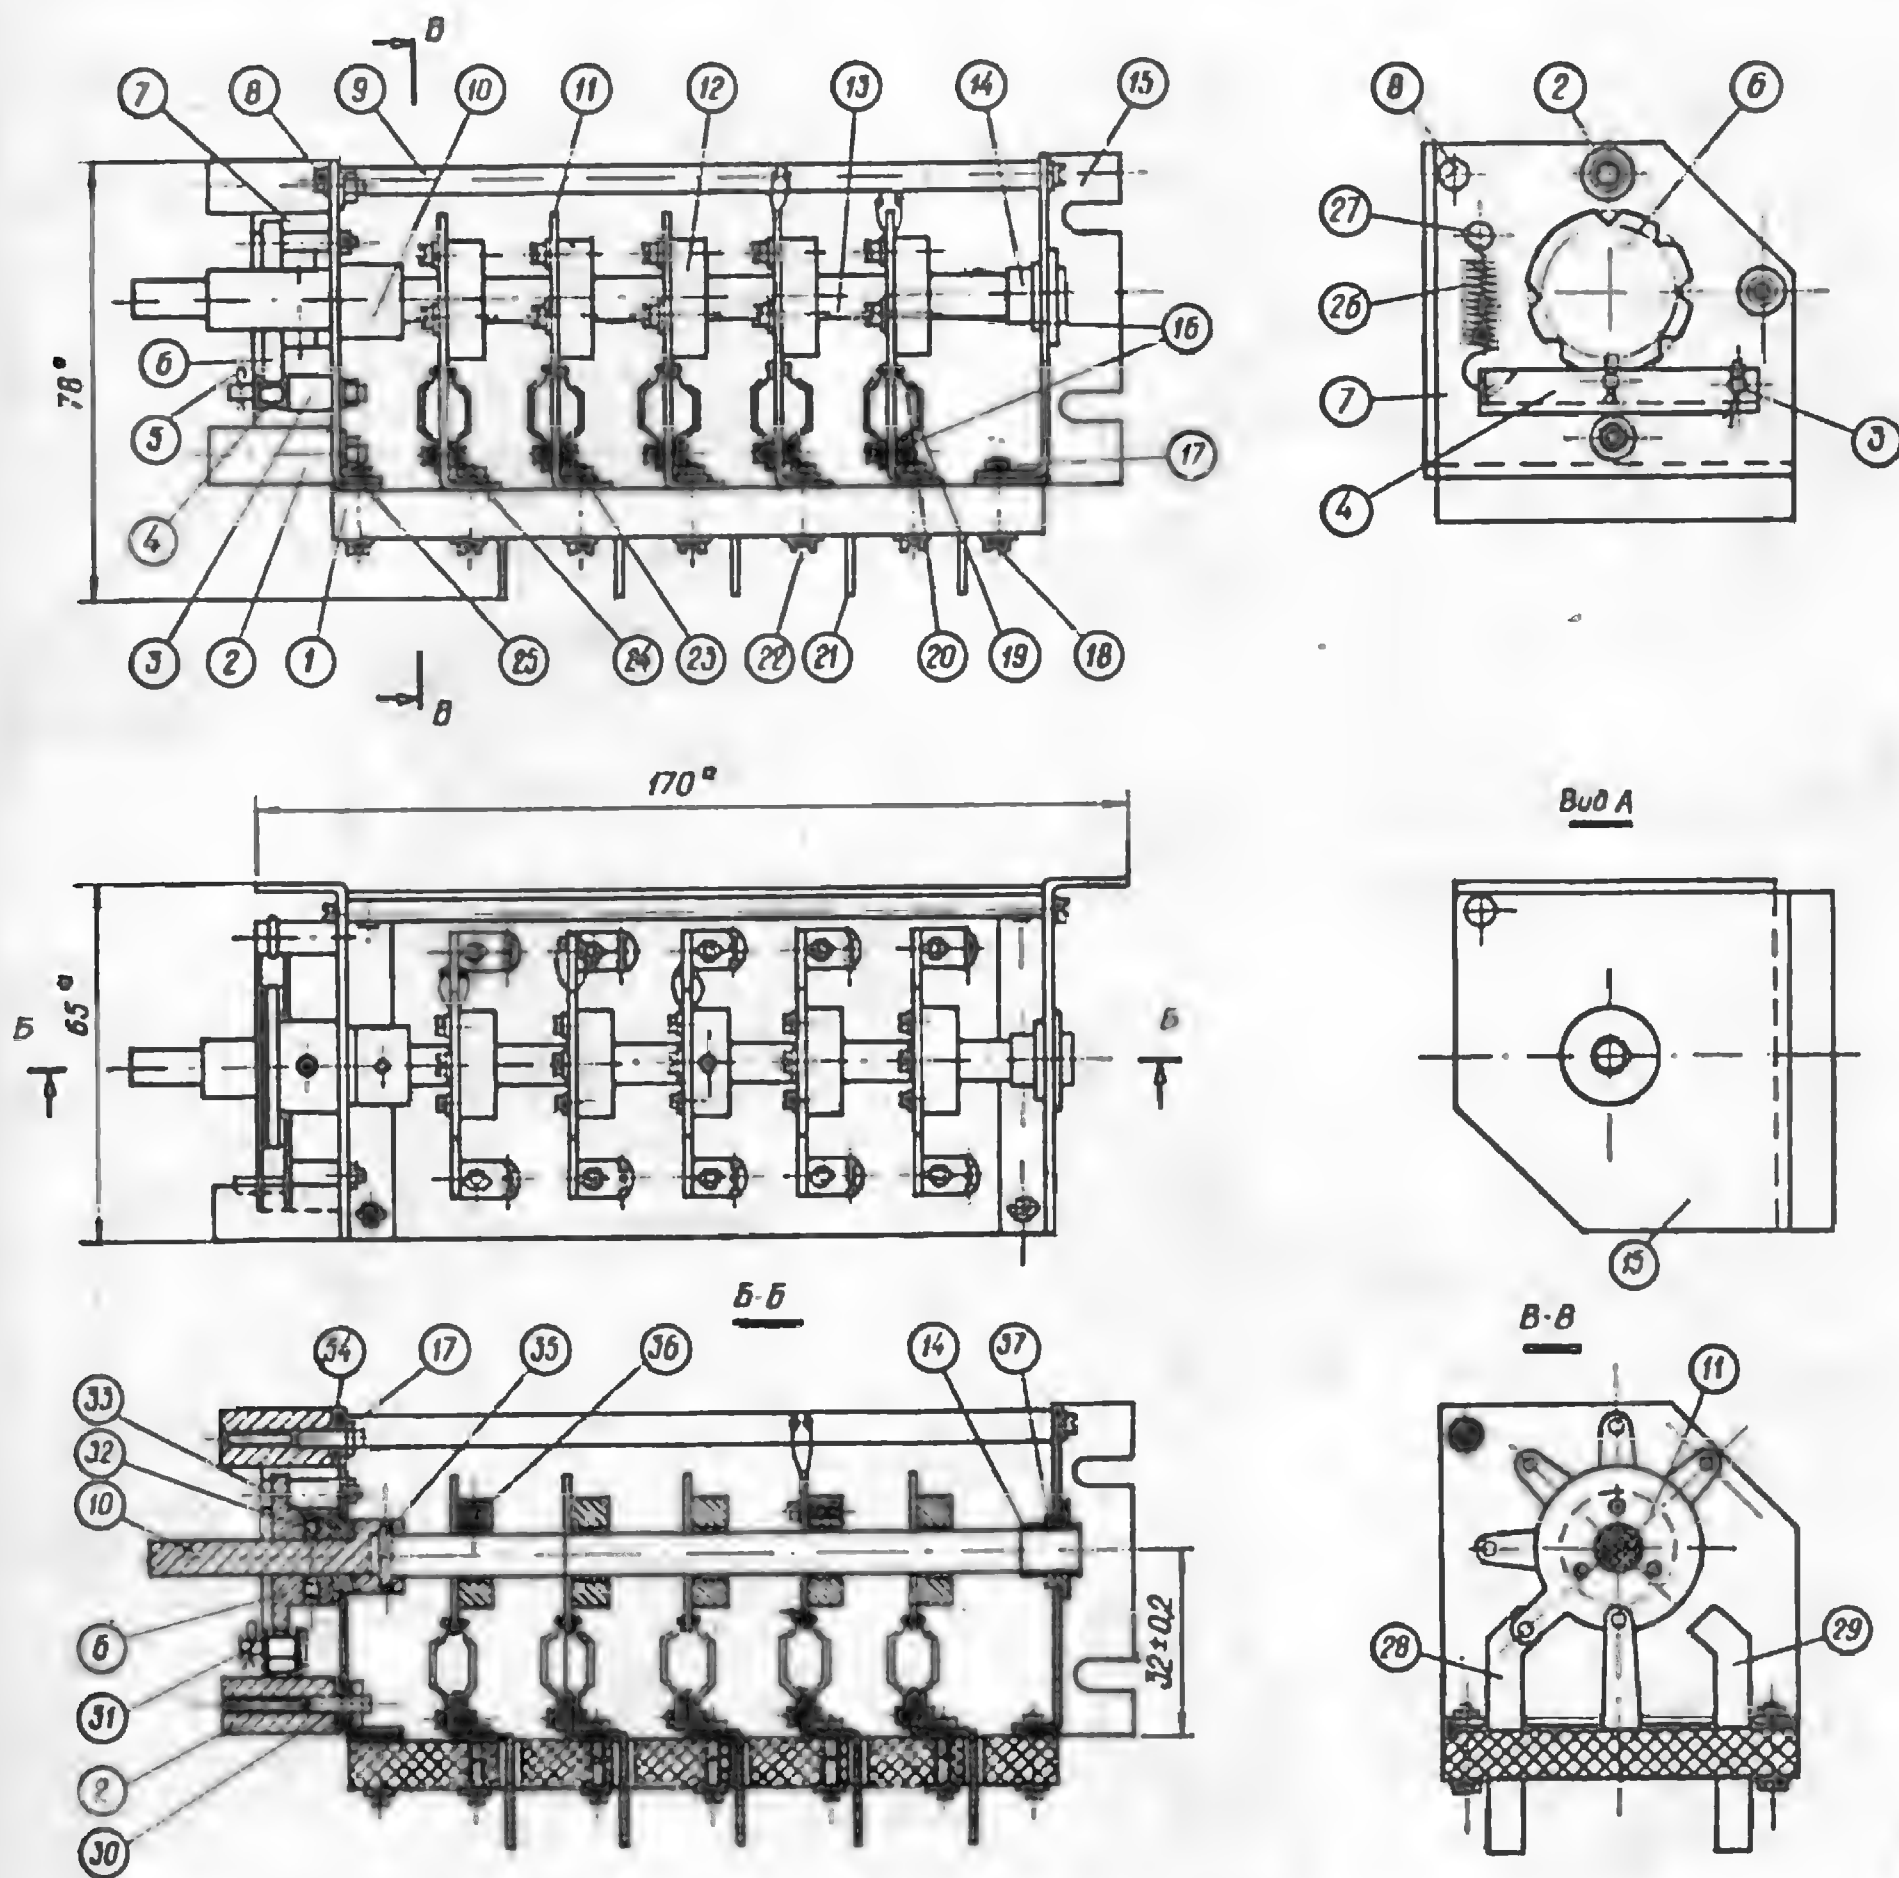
Сборочный чертеж переключателя: 1 — основание; 2 — втулка, Ст. 45, цинковать, затем хромировать, 3 шт.; 3 — ось, Ст. 45, цинковать, затем хромировать; 4 — скоба, Ст. 10кп, цинковать, затем хромировать; 5 — шпилька  $1 \times 8$ , 2 шт.; 6 — звездочка, Ст. 45, цинковать, затем хромировать; 7 — стойка левая, Ст. 10кп, цинковать, затем хромировать; 8 — винт  $M3 \times 6$ , 2 шт.; 9 — стержень, Ст. У8А, цинковать, затем хромировать; 10 — держатель, Ст. 45, цинковать, затем хромировать; 11 — диск, Вр. В2-Т, химически пассанировать, 10 шт.; 12 — фланец, Д16-Т, оксидировать, 3 шт.; 13 — вал, фарфор (органическое стекло, подстирол); 14 — втулка, латунь Л63; 15 — стойка правая, Ст. 10кп, цинковать, затем хромировать; 16 — винт  $M2,5 \times 6$ , 20 шт.; 17 — гайка  $M3$ , 7 шт.; 18 — винт  $M3 \times 16$ , 4 шт.; 19, 20 — ламель, Вр. В2-Т, пассанировать, по 10 шт.; 21 — скоба, латунь Л63Т, серебрить, 3 шт.; 22 — винт  $M2,5 \times 12$ , 15 шт.; 23 — шайба, 65 шт.; 24 — гайка  $M2,5$ , 20 шт.; 25 — прокладка, резина ПМБ-М, 2 шт.; 26 — пружина (рабочих винтов 11, направления навалки — право), проволока стальная класса II диаметром 0,5 мм, надмировать, затем хромировать; 27 — ось, Ст. 45, цинковать, затем хромировать; 28 — контакт правый, латунь Л63Т, серебрить, 5 шт.; 29 — контакт левый, латунь Л63Т, серебрить, 5 шт.; 30 — шпилька  $M3 \times 16$ , 3 шт.; 31 — ось, Ст. 45, цинковать, затем хромировать; 32 — винт  $M3 \times 4$ , 4 шт.; 33 — втулка, Ст. 45, цинковать, затем хромировать; 34 — шайба, 11 шт.; 35 — штифт цилиндрический диаметром 3 длиной 12 мм; 36 — винт  $M3 \times 5$ , 10 шт.; 37 — втулка, Ст. 45, цинковать, затем хромировать
